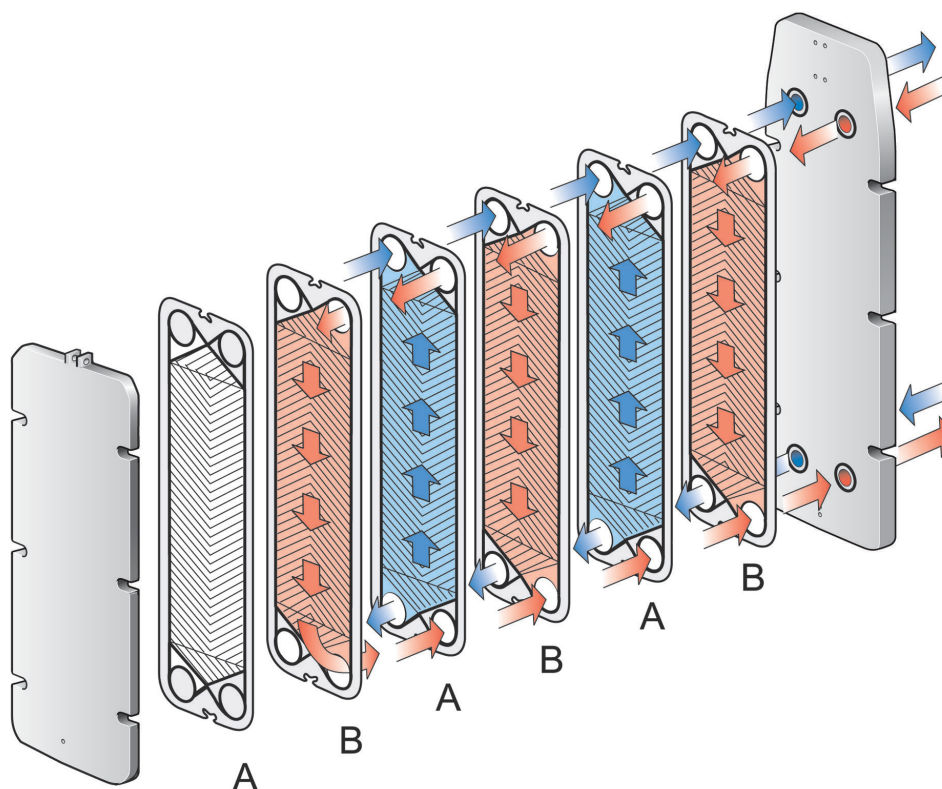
Princípio da disposição do conjunto de placas, juntas voltadas para a placa de pressão.
